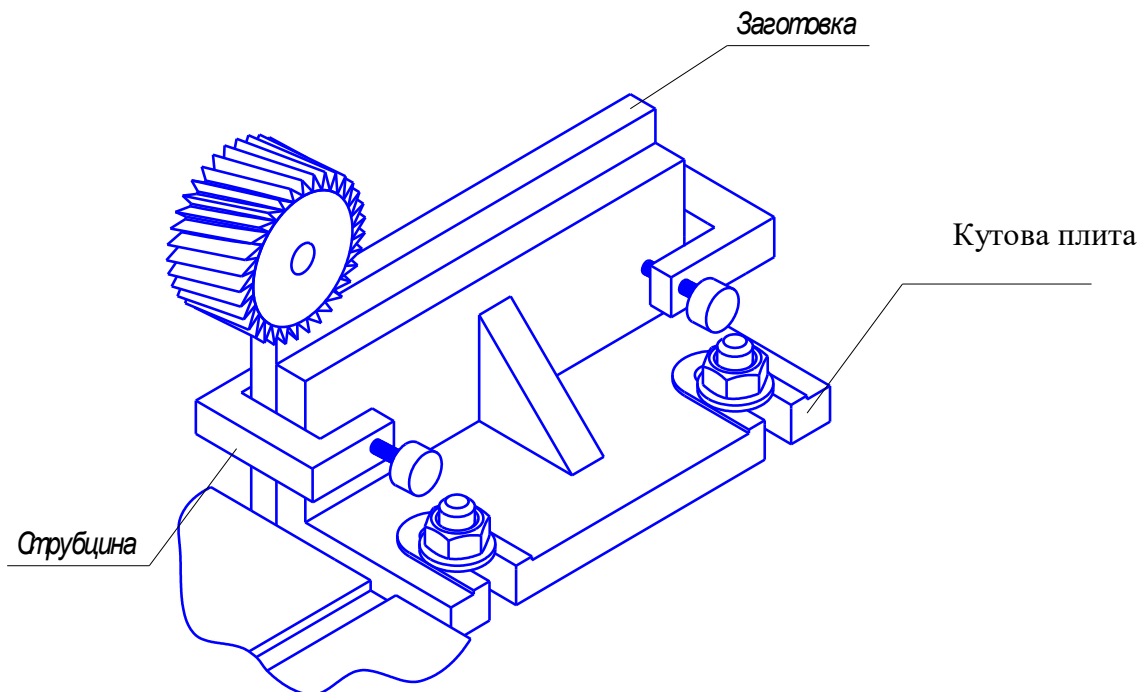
Встановлення заготовки за допомогою кутової плити на столі фрезерного верстата
